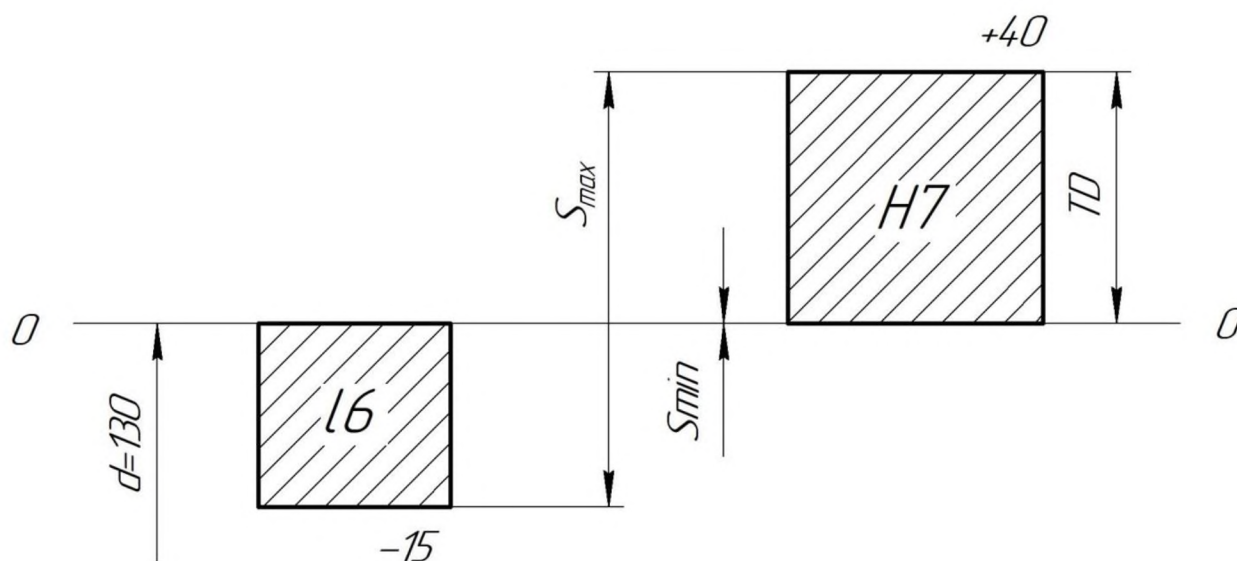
Схема полів допусків з'єднання з підшипником
